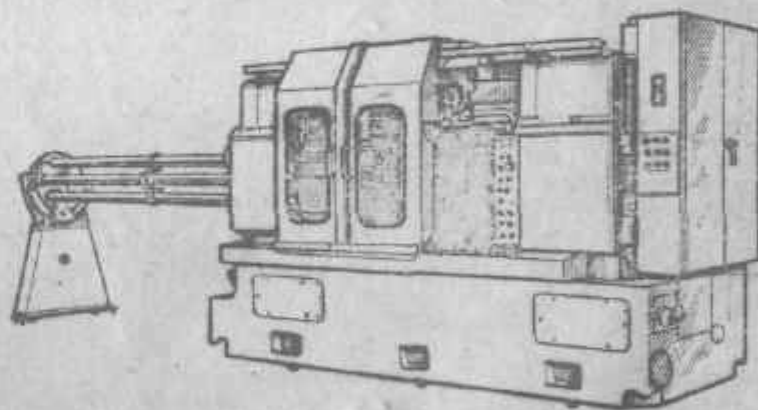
Автомат токарный шестিশпиндельный прутковый горизонтальный мод. 1Б240-6(6К)
